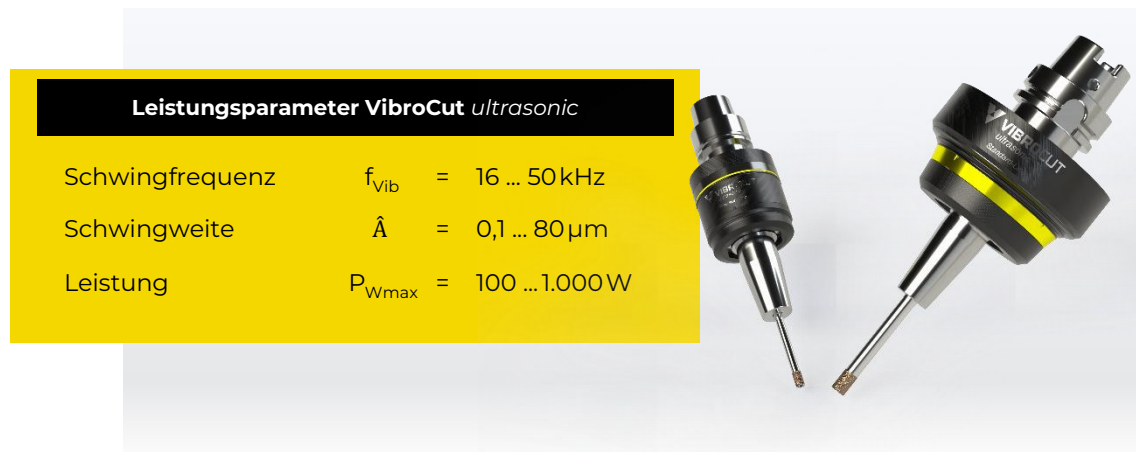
Ultraschall-Werkzeughalter für VibroCut *ultrasonic
